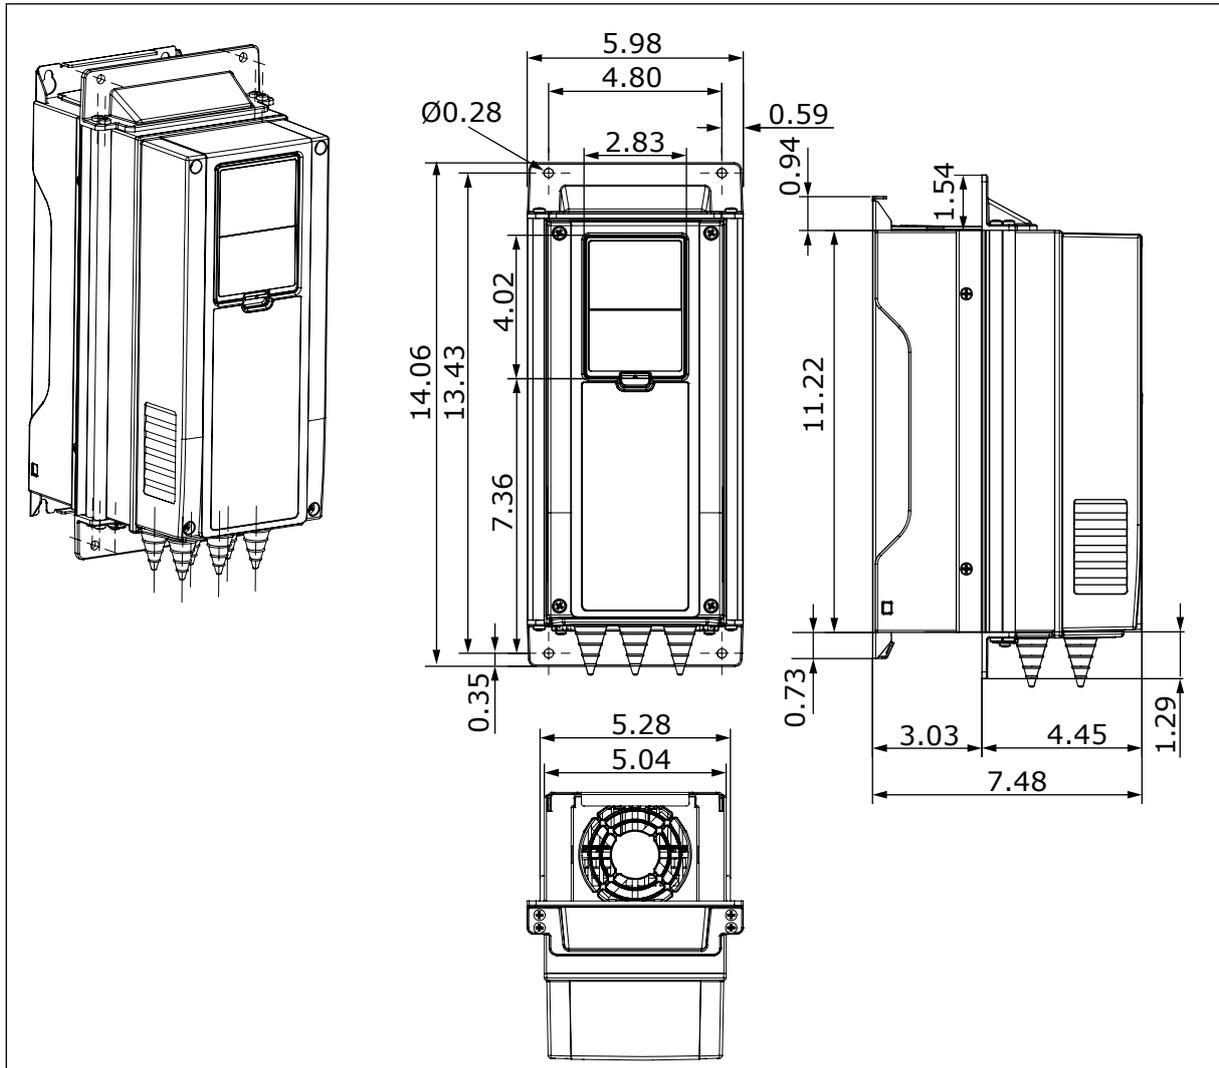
Abmessungen des Frequenzumrichters, Flanschbefestigung, MR4 [in]
